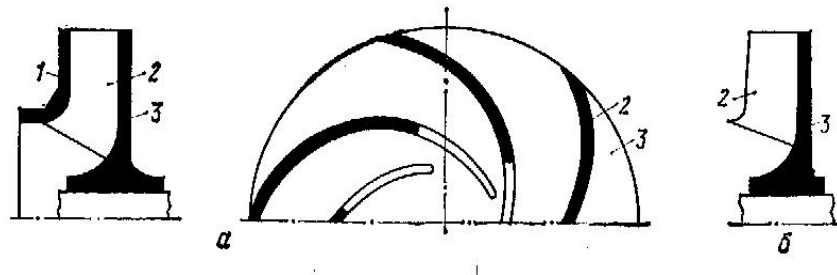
Робочі колеса: 1-покривний диск; 2-лопать; 3-основний диск
